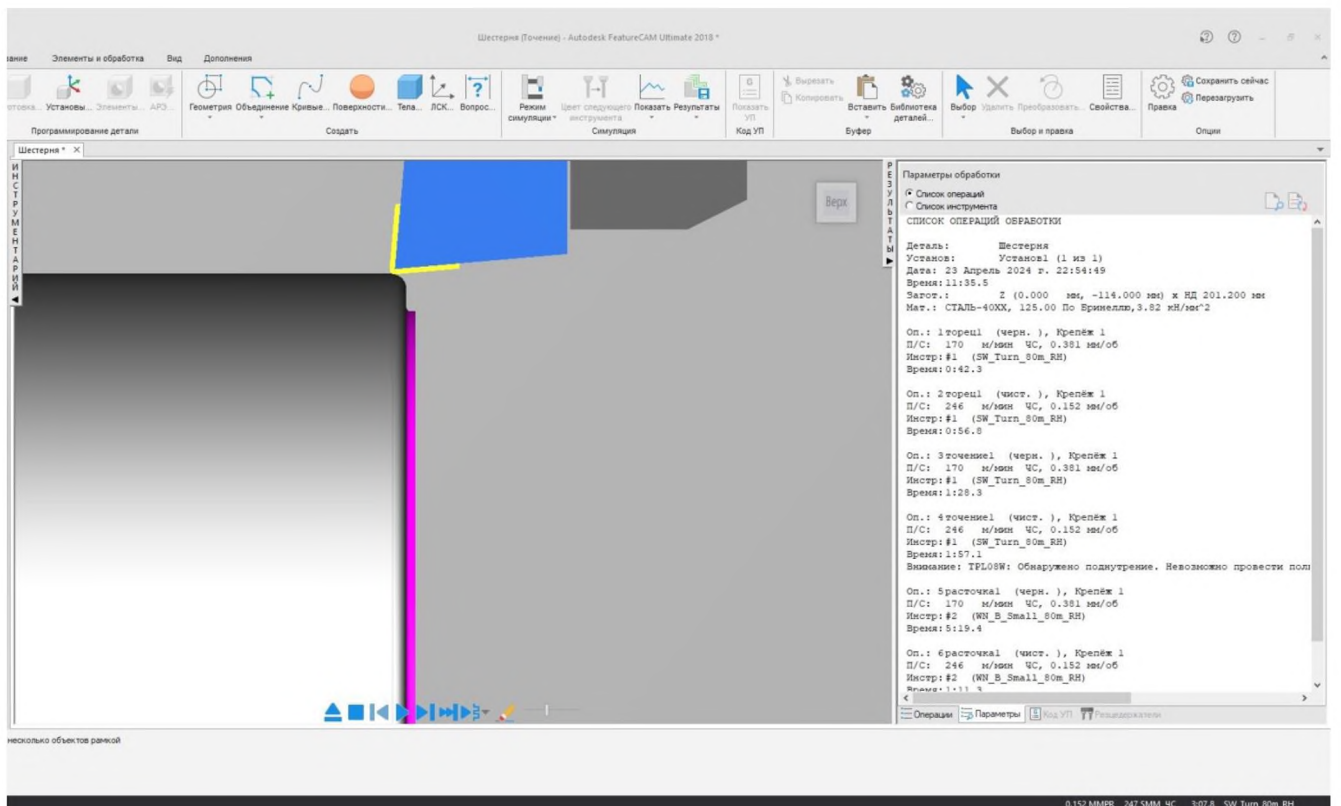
Процес обробки деталі «Шестерня» на віртуальному верстаті у Feature CAM – точіння поверхні
